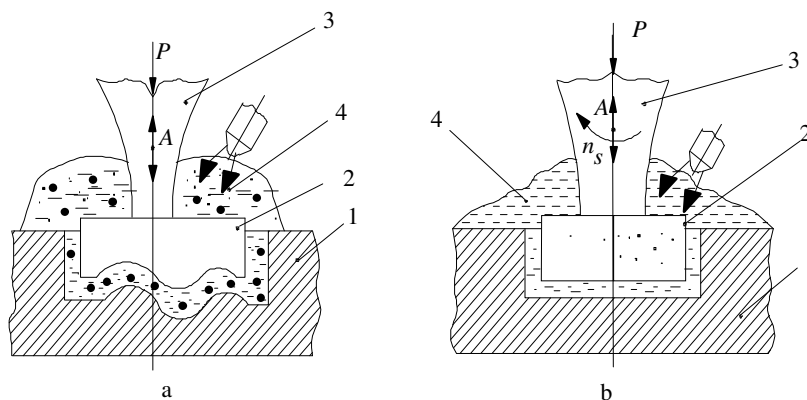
Schema de principiu la prelucrarea dimensională cu ultrasunete:
